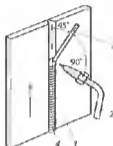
Сварка вертикального шва снизу вверх (левый способ):
